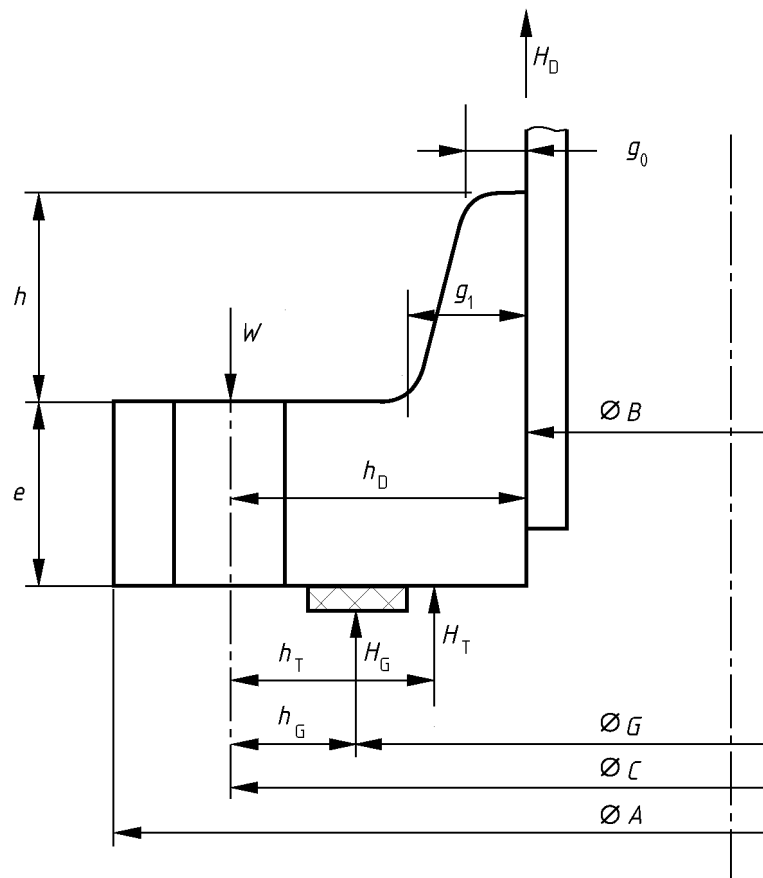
Brida de cara estrecha - tipo de cubo deslizante
